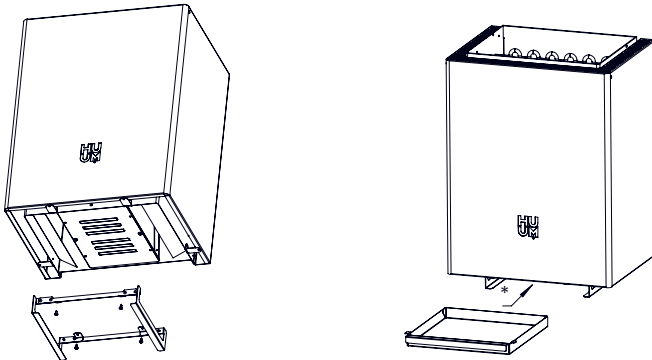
ábra A HUUM CORE Wall és a CORE Wall Mini hőterelőjének telepítése.
